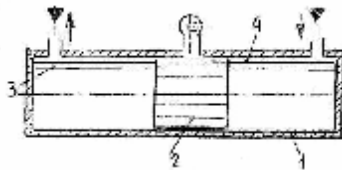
Схема бесштокового пневмоцилиндра:
